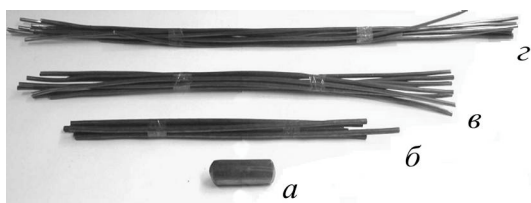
Заготовки из титана Grade 2 на различных стадиях изготовления
